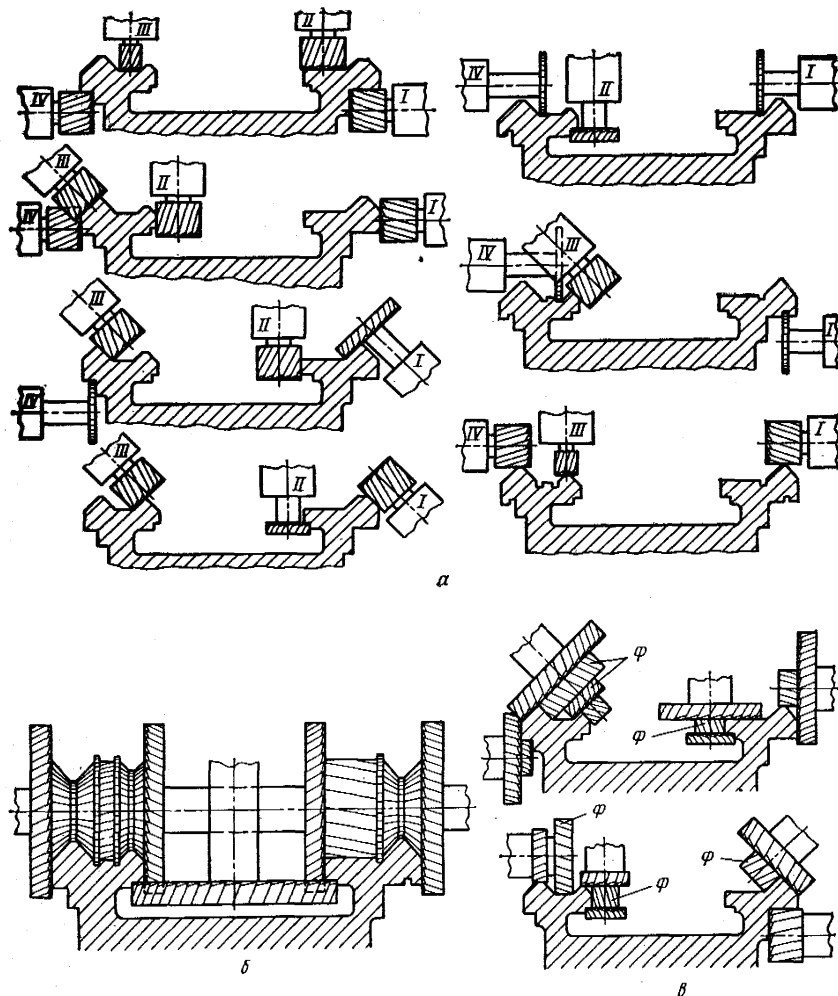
Способи фрезерування прямолінійних напрямних заготовки: а – стандартними фрезами; б – спеціальним набором фрез; в - декількома наборами фрез; φ – спеціальні фрези в наборі
